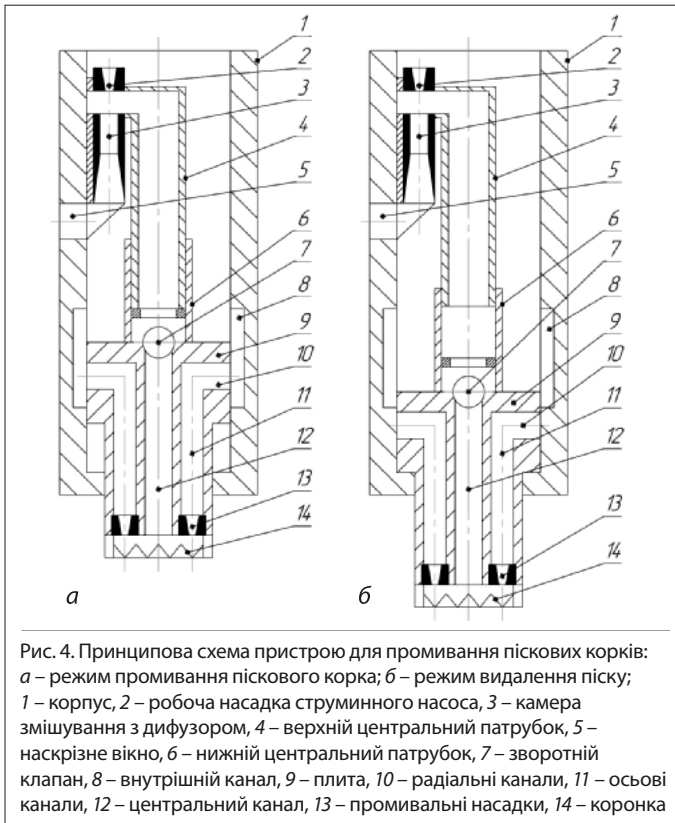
Принципова схема пристрою для промивання піскових корків: а – режим промивання піскового корка; б – режим видалення піску; 1 – корпус, 2 – робоча насадка струминного насоса, 3 – камера змішування з дифузором, 4 – верхній центральний патрубок, 5 – наскрізне вікно, 6 – нижній центральний патрубок, 7 – зворотній клапан, 8 – внутрішній канал, 9 – плита, 10 – радіальні канали, 11 – осьові канали, 12 – центральний канал, 13 – промивальні насадки, 14 – коронка
